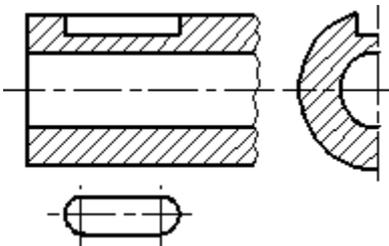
Образец оформления плавного перехода от одной поверхности к другой
